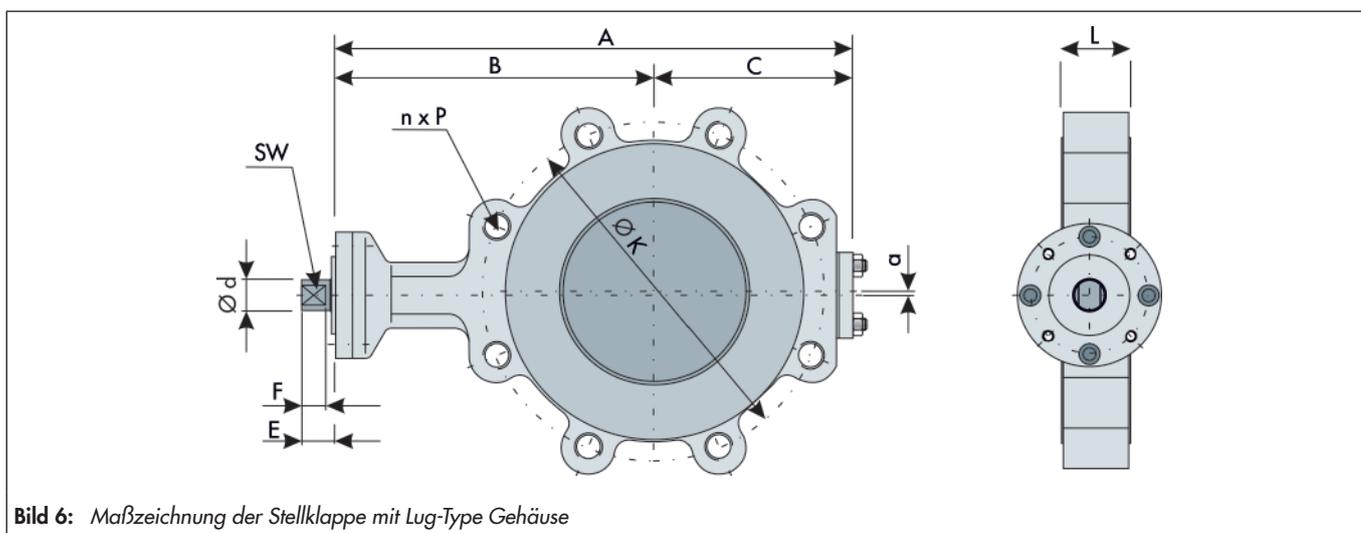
Maßzeichnung der Stellklappe mit Lug-Type Gehäuse
